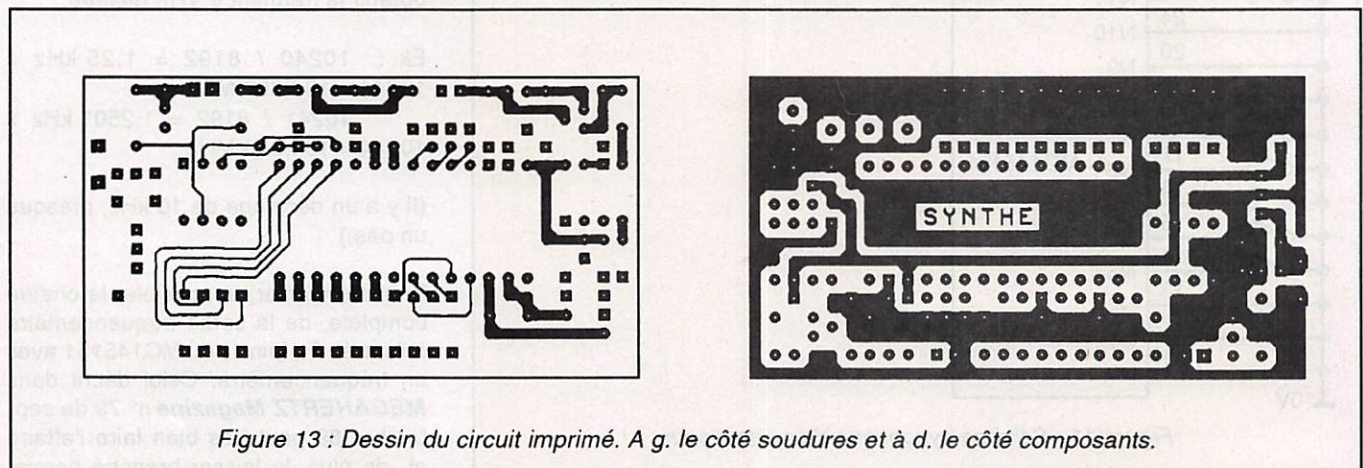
Dessin du circuit imprimé. A g. le côté soudures et à d. le côté composants.
